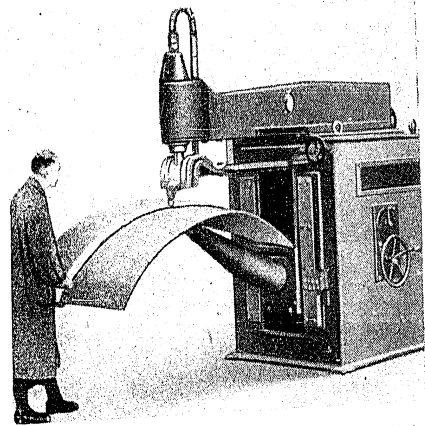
Elektrische Punktschweißmaschine in Tätigkeit
